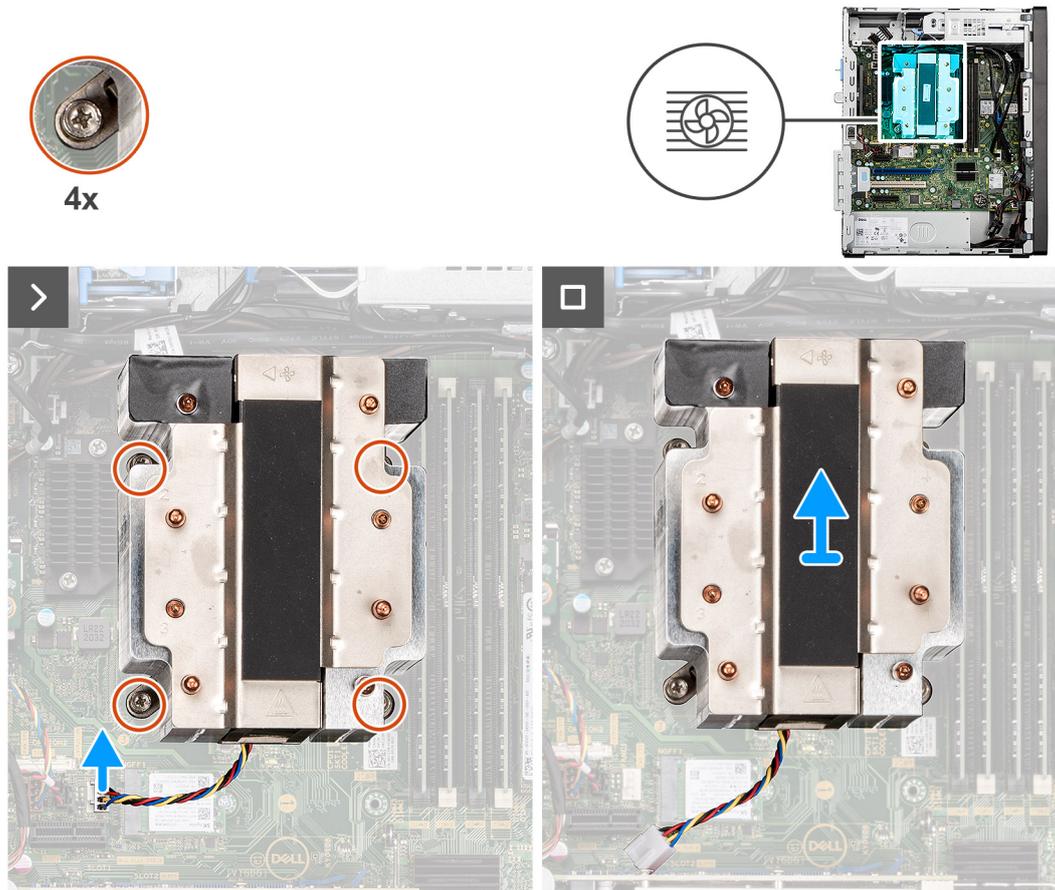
Entfernen der Lüfter- und Kühlkörperbaugruppe (für 125-W-Prozessoren)
